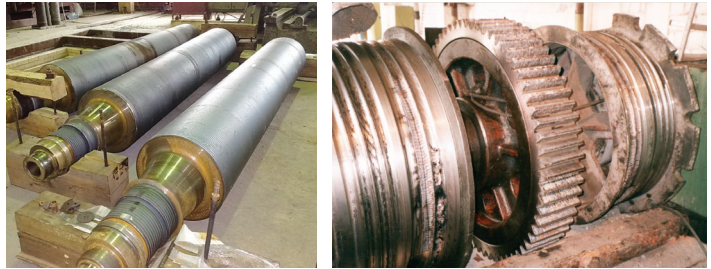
Канатные барабаны и приводная шестерня редуктора «напора» экскаватора ЭКГ-8А, упрочненные плазменной закалкой.
